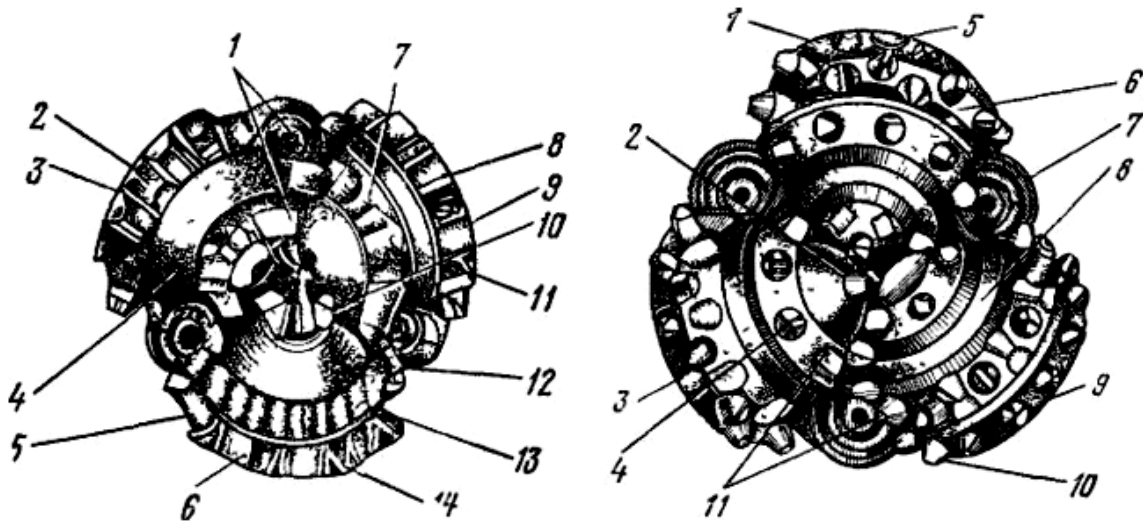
Елементи долота із зубами, що фрезеруються, і вставками з карбиду вольфраму: 1, 7 - вершина і підстава зубця 2 - зубець; 3, 6, 8 - шарошки, 4 - міжвінцове розточування, 5 - виймка між зубцями 9 - промивальна канавка 10 - стисоподібна вершина; 11, 14 - калібруючі поверхні периферійних зубців з різальними кромками відповідно L і T - образної форми, 12 - тильна сторона шарошки з твердим покриттям; 13 - напрямної шарошки; 1, 3, 9 - шарошки № 2, 1 і 3 відповідно, 2 - штирі з пікоподібною робочою голівкою, 4 - подовжені штирі з пікоподібною робочою голівкою; 5 - плоскі твердосплавні вставки; 6 - крок (змінний) між твердосплавними вставками; 7 - отвір насадки; 8 - міжвінцове розточування (канавка); 10 - штирі з пікоподібною робочою голівкою калібруючого вінця шарошки, 11 - штирі внутрішнього вінця шарошки.
